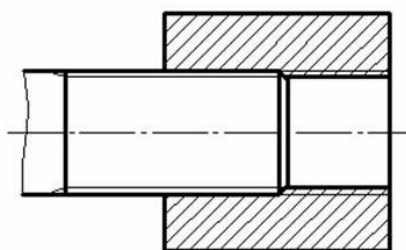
Изображение резьбы резьбового соединения на разрезе
